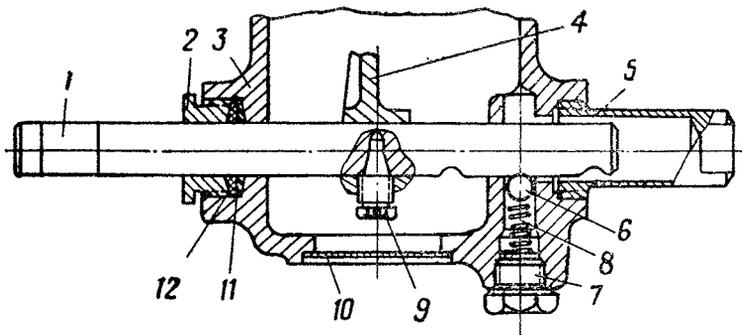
Фиксаторный механизм коробки отбора мощности привода водометного движителя:
